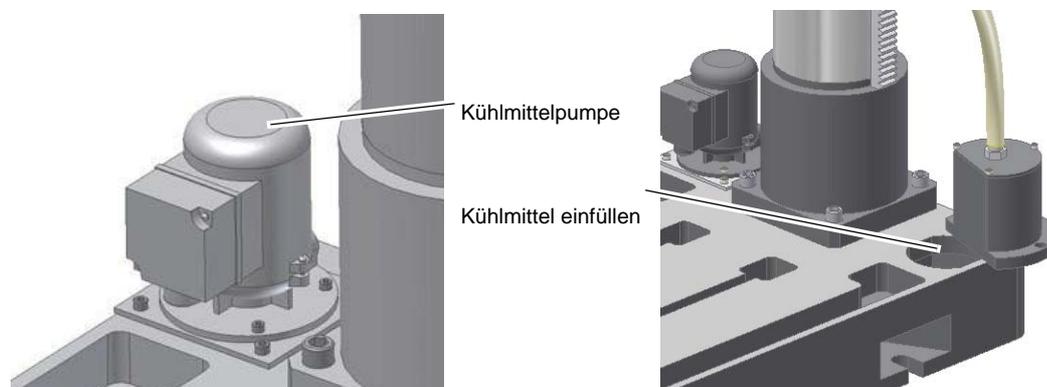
Kühlmittelpumpe, Kühlmittel Einfüllöffnung
